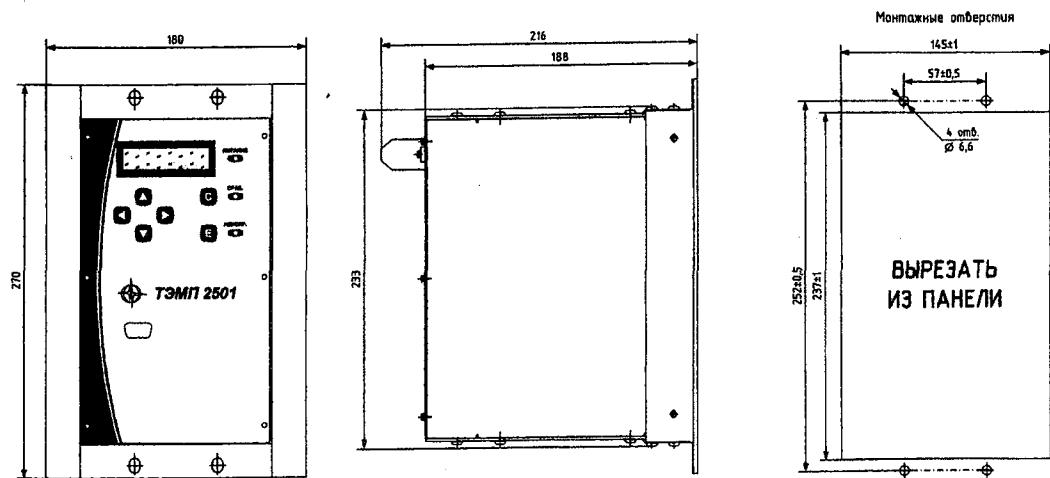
Габаритные и установочные размеры ТЭМП 2501-13/23/43
